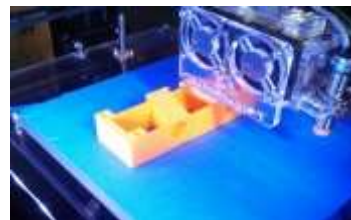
Impresión del cuerpo del sensor en la impresora 3D.
